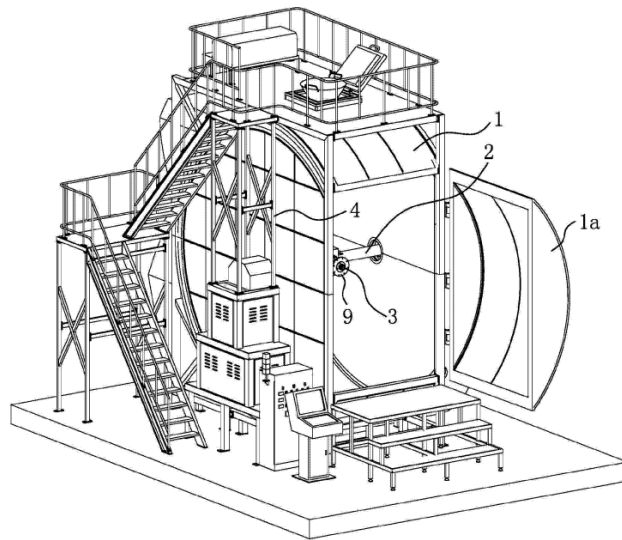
Imagem da máquina de rotomoldagem de uma patente (CN107558611A)
